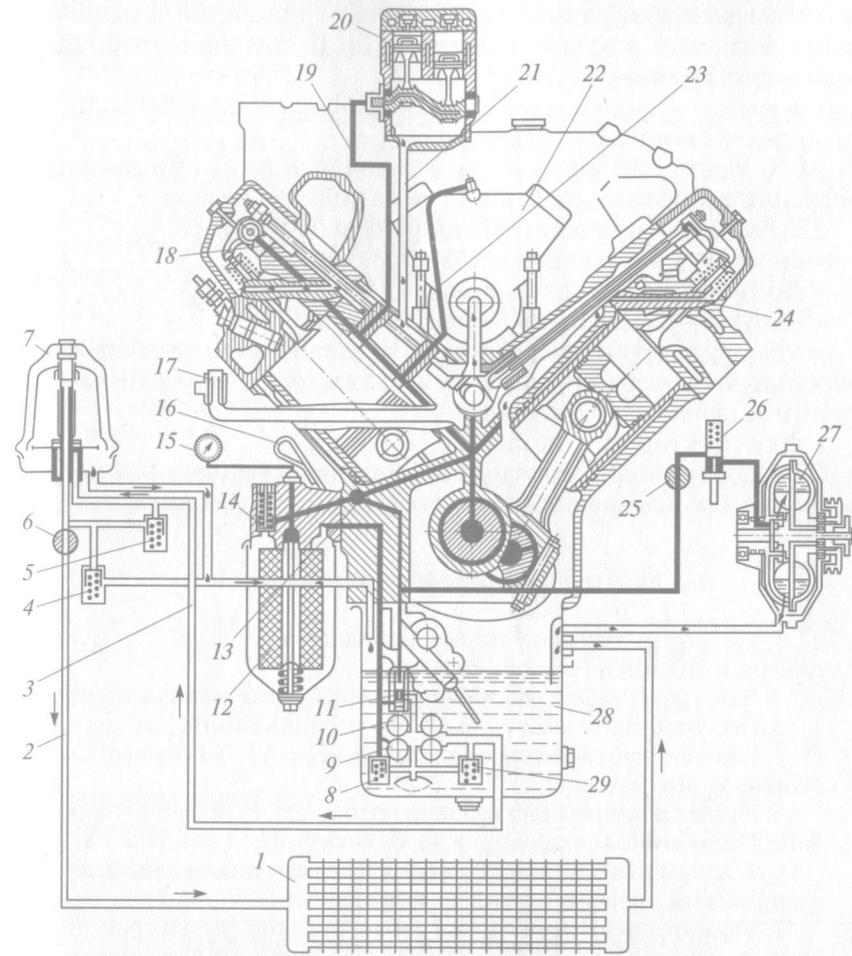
Смазочная система двигателя автомобиля КамАЗ-740:
